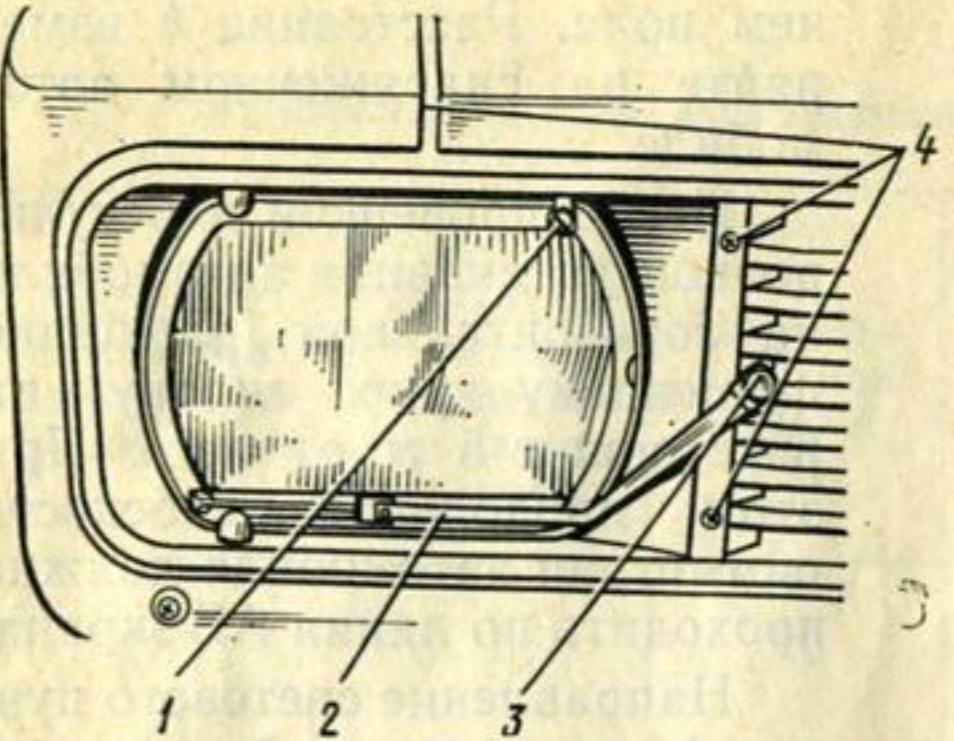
Крепление облицовки радиатора и очистителей фар:
